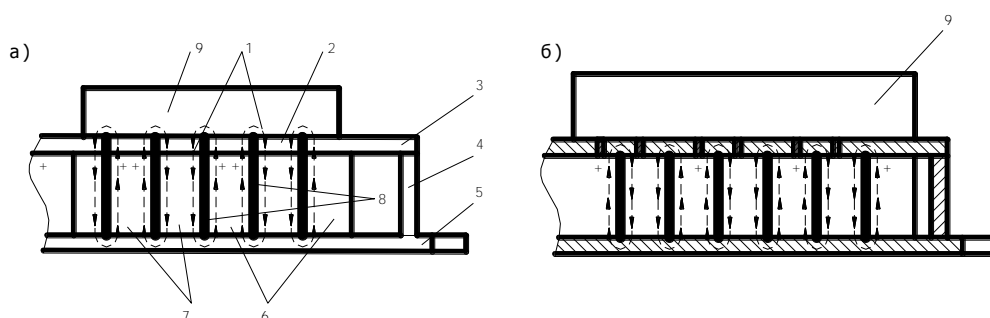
Положение блоков плит с постоянными магнитами: а – при закреплении детали; б – при освобождении детали. 1 – прослойки из немагнитного материала;
